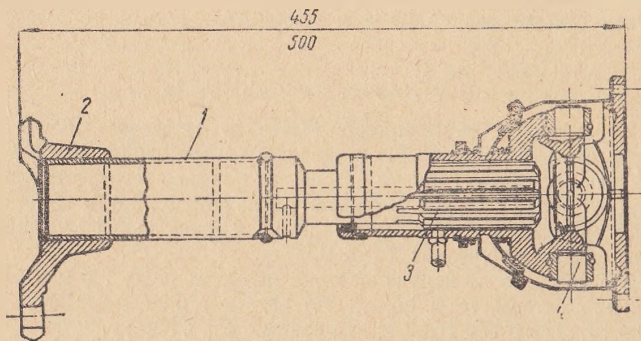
Передний нижний карданный вал «ЗИС-11».
